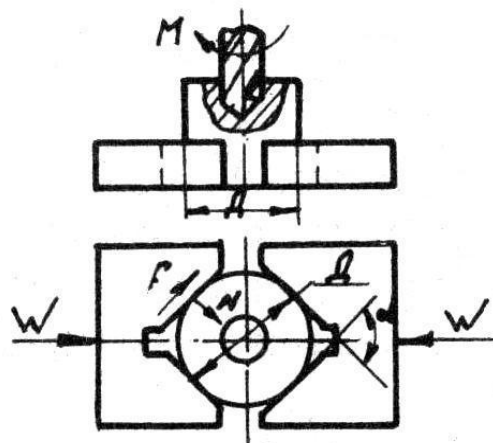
Схема розрахунку затискних зусиль при обробці заготовки на свердлильному верстаті установленій на дві призми.
